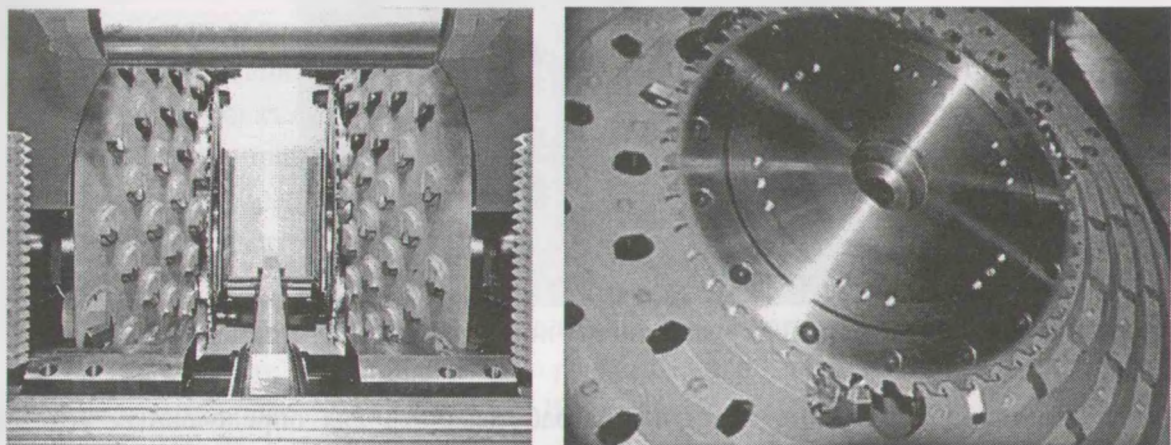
Торцово-конические фрезы фрезерно-брусующих станков
